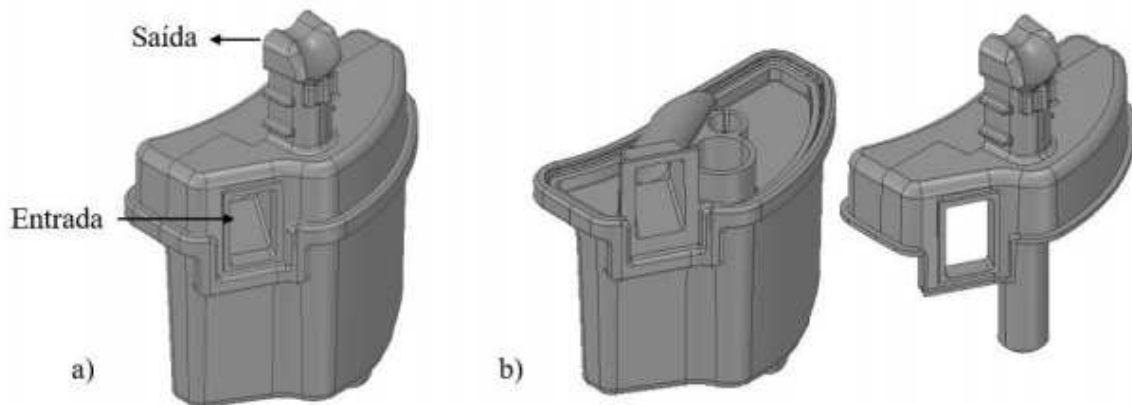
Vista frontal de um filtro acústico montado (a) e desmontado (b)
